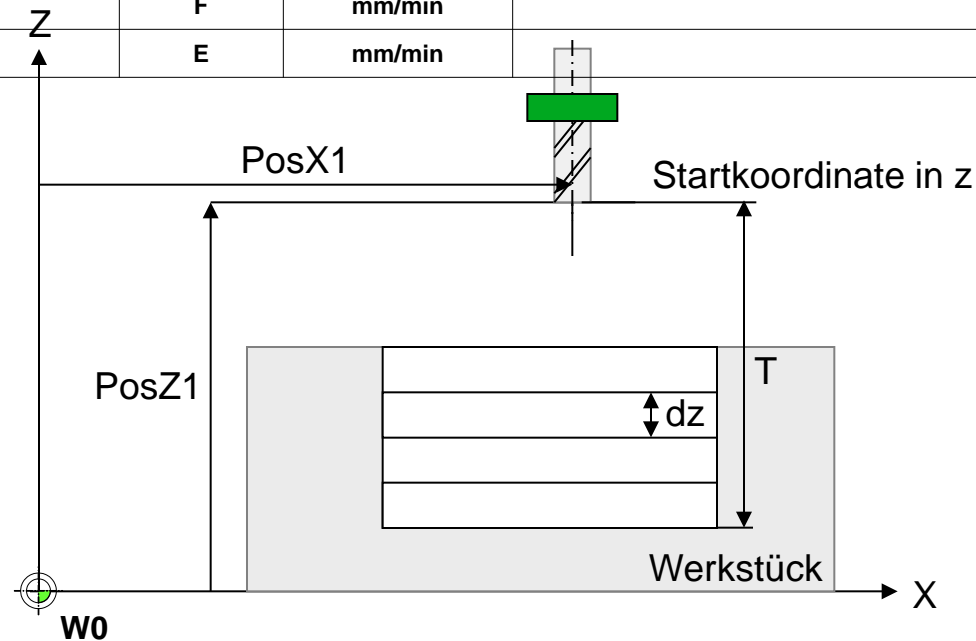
Parameter für die Definition einer rechteckigen Frästasche
